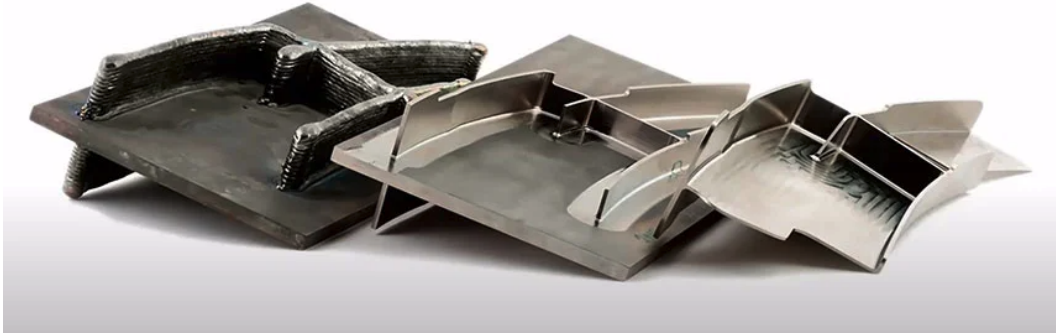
Peça produzida por MADA e usinada por fresamento para obter o acabamento final. Fonte: (3DPRINTING, 2021)
